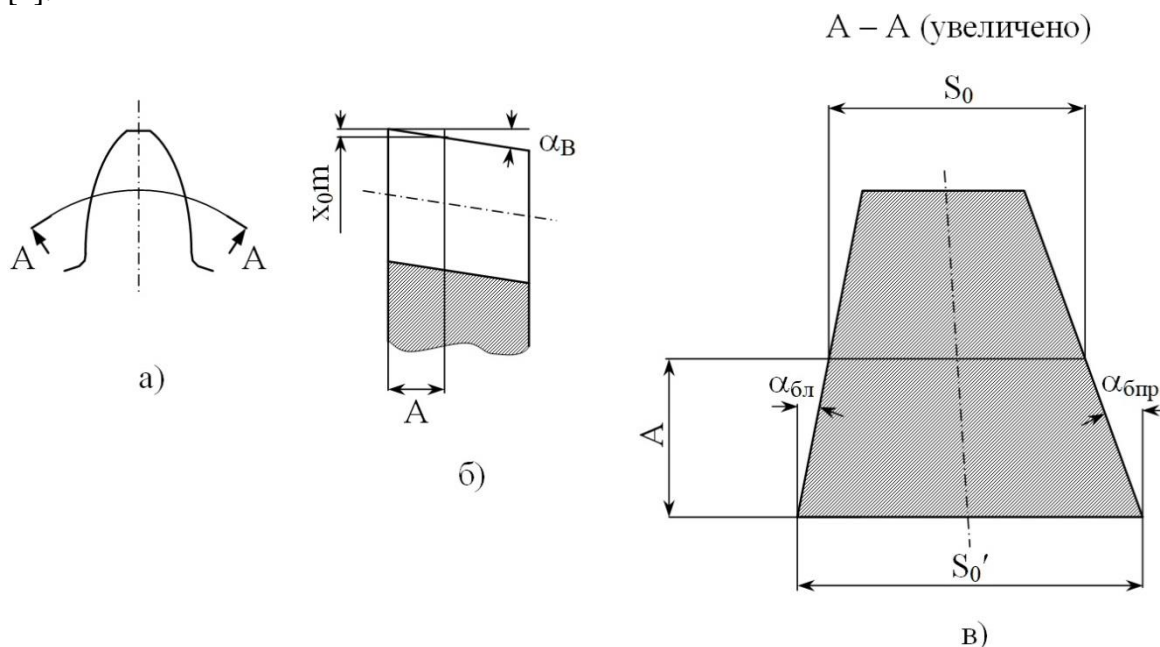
Зуб долбяка с неравными боковыми задними углами:
